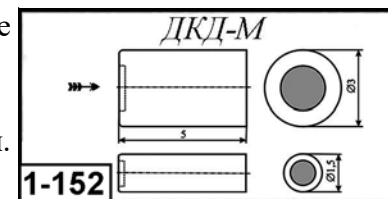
Внешний вид и габаритные размеры детектора ДКД-М
